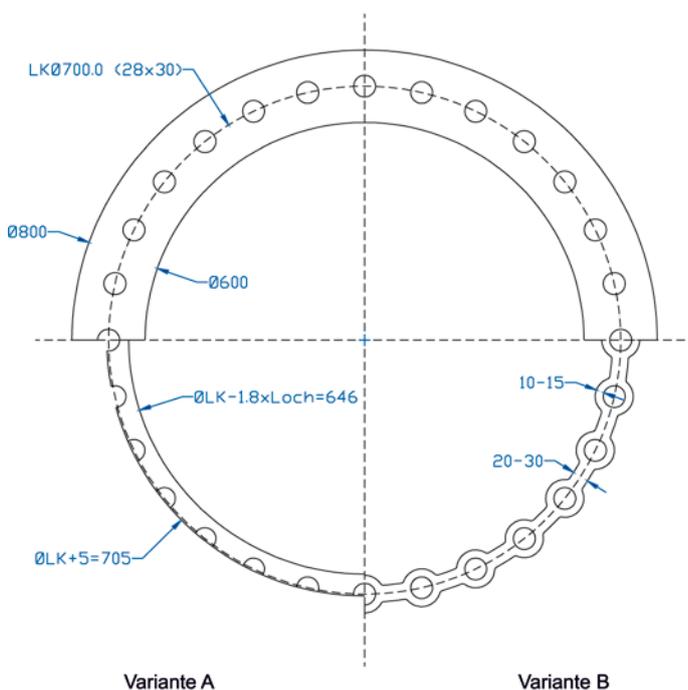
Beispiel für die Optimierung einer Dichtungsgeometrie
